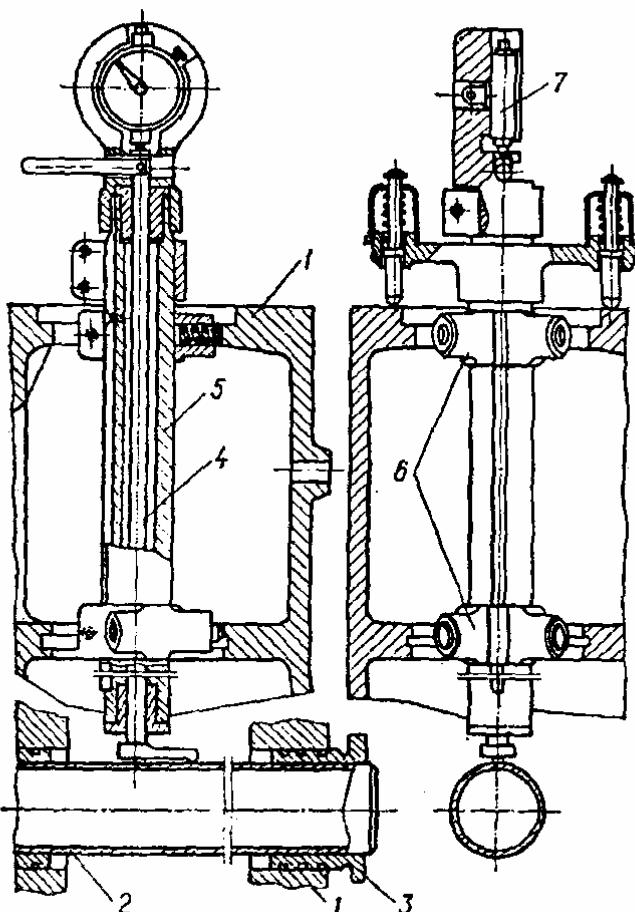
Схема перевірки перпендикулярності осей отворів блока під гільзи до привалкової площини блока і до загальної осі опор колінчастого вала: 1 – блок циліндрів; 2 – оправка; 3 – втулка (дві); 4 – плунжер; 5 – колонка; 6 – самовставні фіксатори; 7 – індикаторна головка
